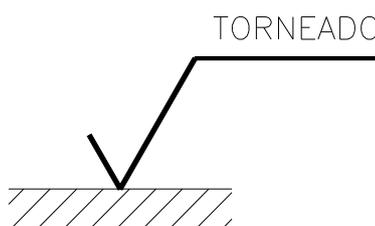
símbolo de estado de superfície com indicação do método de fabricação.
